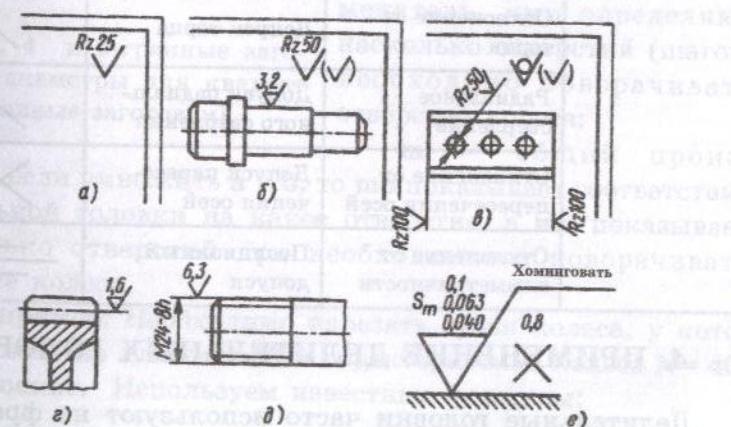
Обозначение шероховатости поверхности (по О'з DST 646-95).
